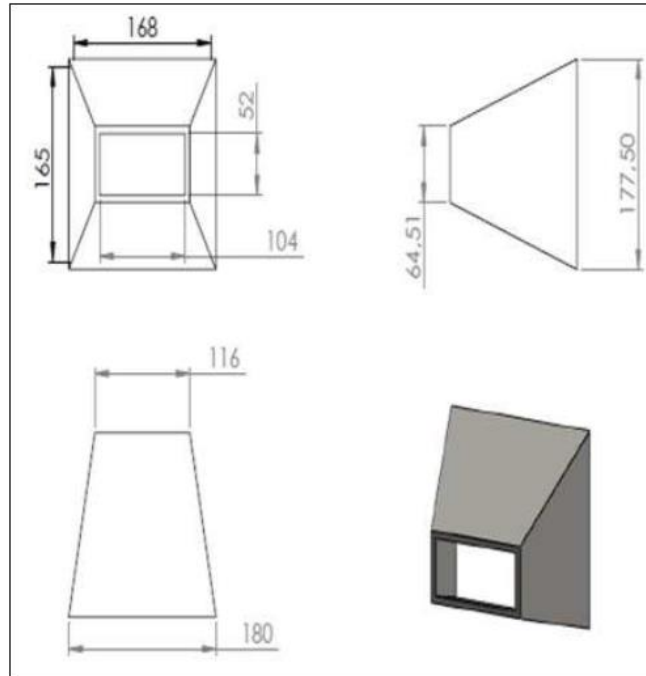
Dimensiones de la boca moldeadora, con las medidas en mm. Fuente: (Arroyo, 2016)
